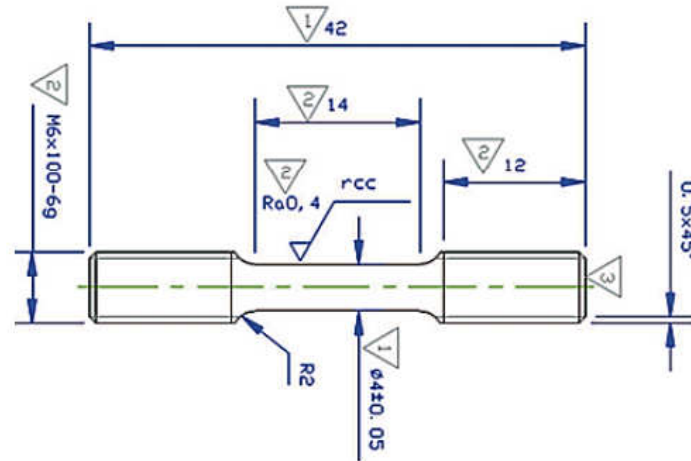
Dimensions des éprouvettes de traction/fluage
